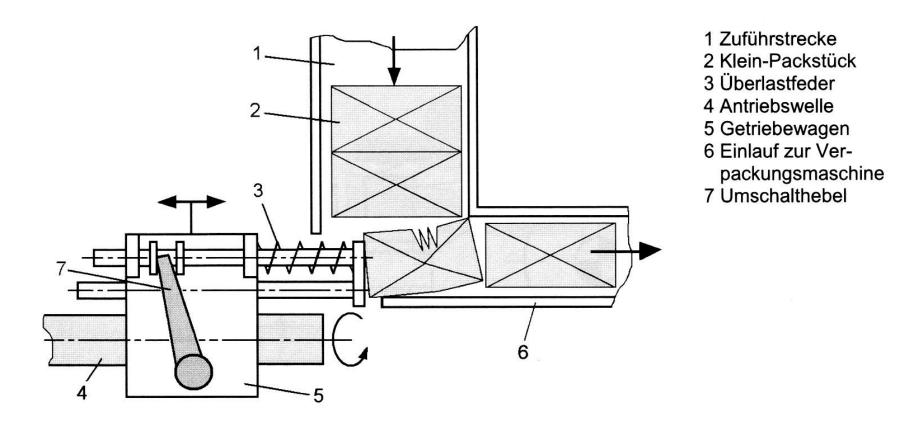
Schieber mit Rollringgetriebe an einer Schachtelzuführung (Uhing; www.uhing.com)
